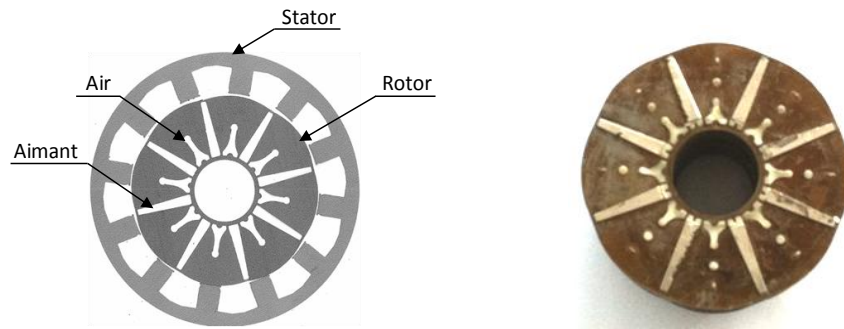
Géométrie de la machine synchrone – Vue de face du rotor
